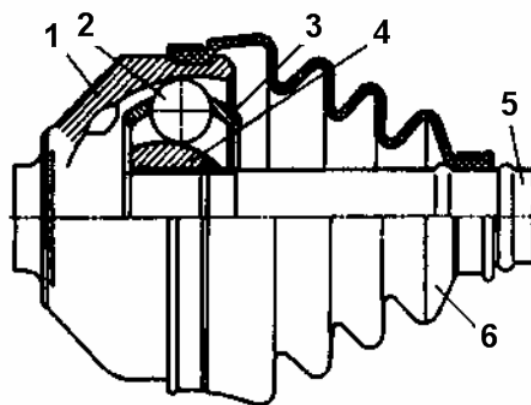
Шестишариковый карданный шарнир: 1 – корпус; 2 – шарик; 3 – сепаратор; 4 – кулачок; 5 – вал; 6 – защитный чехол
